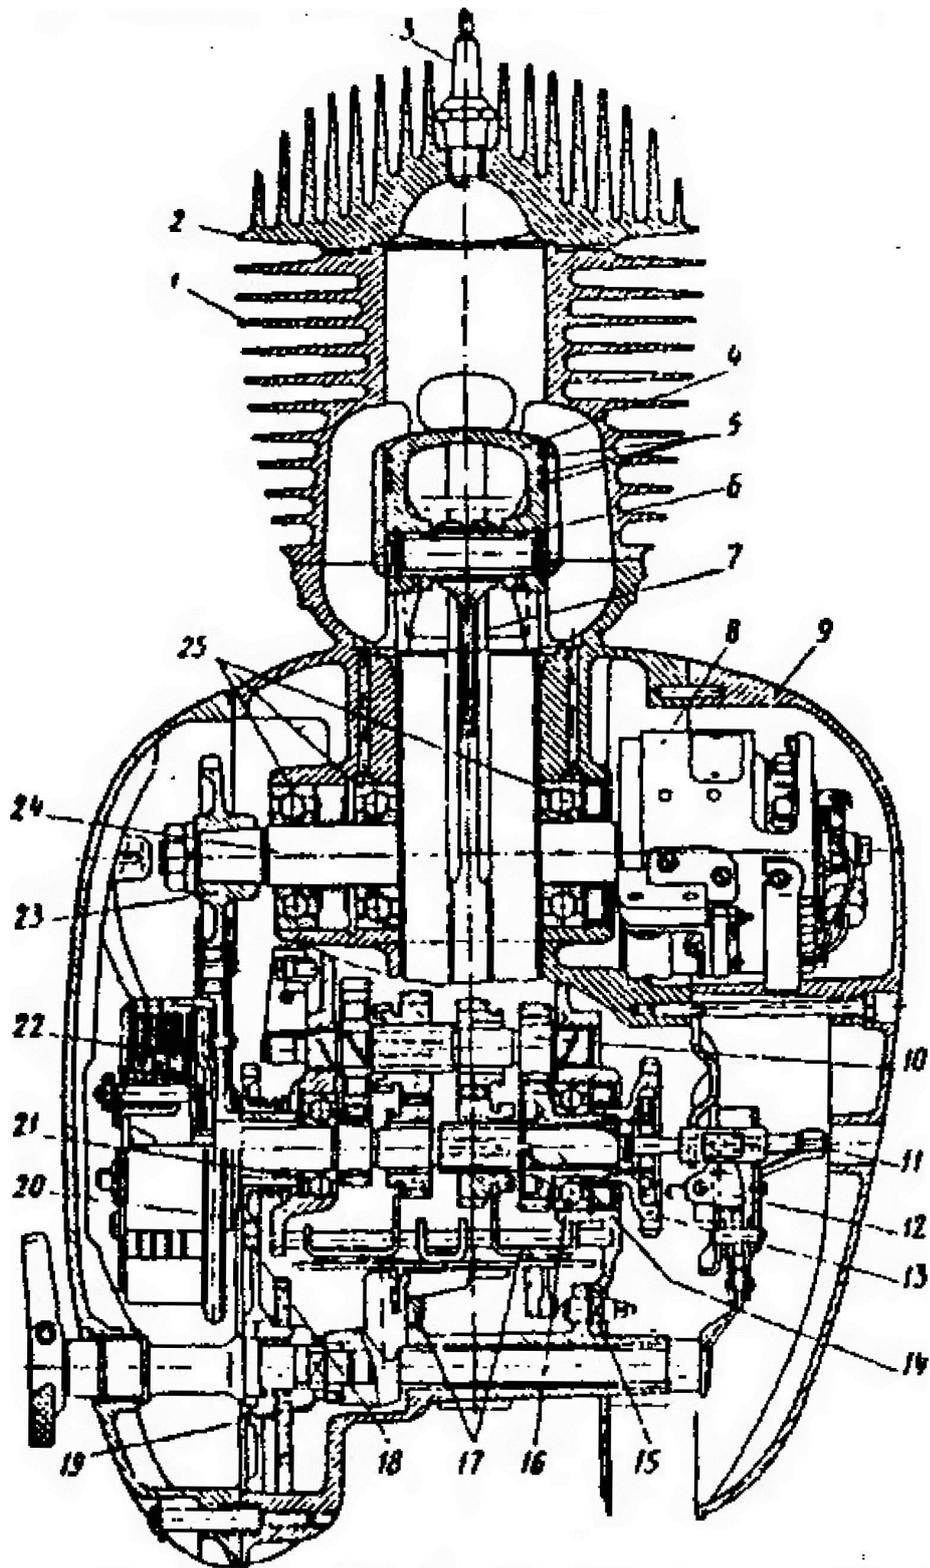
Поперечный разрез силового агрегата мотоциклов "Ява-250" модели 559/04 и модели 559/07: 1 - цилиндр; 2 - головка; 3 - свеча зажигания; 4 - поршень; 5 - поршневые кольца; 6 - палец; 7 - шатун; 8 - генератор; 9 - правая крышка картера; 10 - промежуточный вал коробки передач с шестернями; 11 - регулировочный болт сцепления; 12 - механизм автоматического выключения сцепления; 13 - ведущая звездочка задней передачи; 14 - первичный вал коробки передач с шестернями; 15 - контакт указателя нейтральной передачи; 16 - подшипник 6205 вторичного вала; 17 - вилки переключения передач; 18 - пусковой сектор; 19 - вал переключения передач; 20 - храповая шестерня; 21
